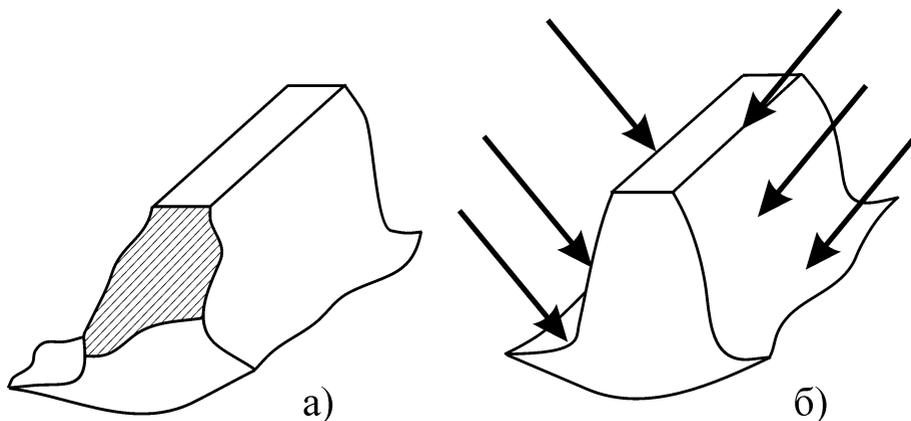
Износ зубчатых передач: а) скол зуба; б) зона осмотра зубьев
